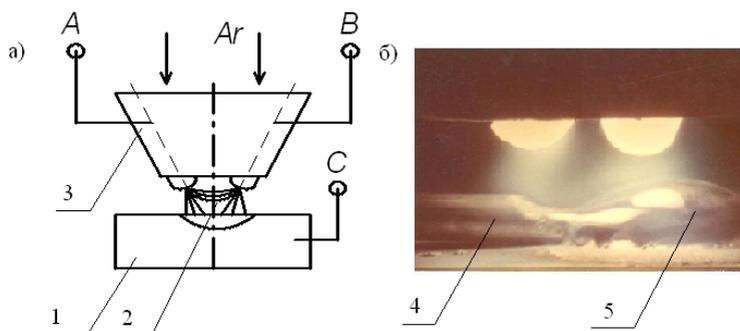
Процесс горения трехфазной дуги в среде аргона с неплавящихся электродов: *а* – схема горения трехфазной дуги (*1* – изделие; *2* – факел трехфазной дуги; *3* – сварочная горелка); *б* – реальный процесс (*4* – присадочный пруток; *5* – сварной шов)
